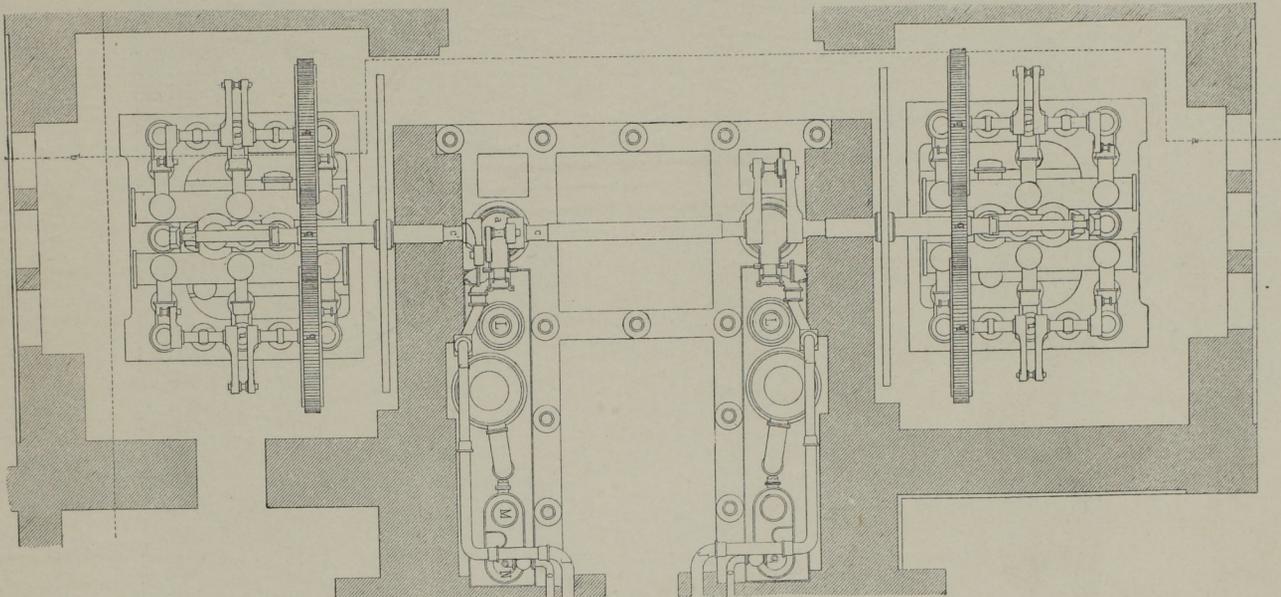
Grundriss der Maschinen und Pumpen. Masst. 1 : 90.
